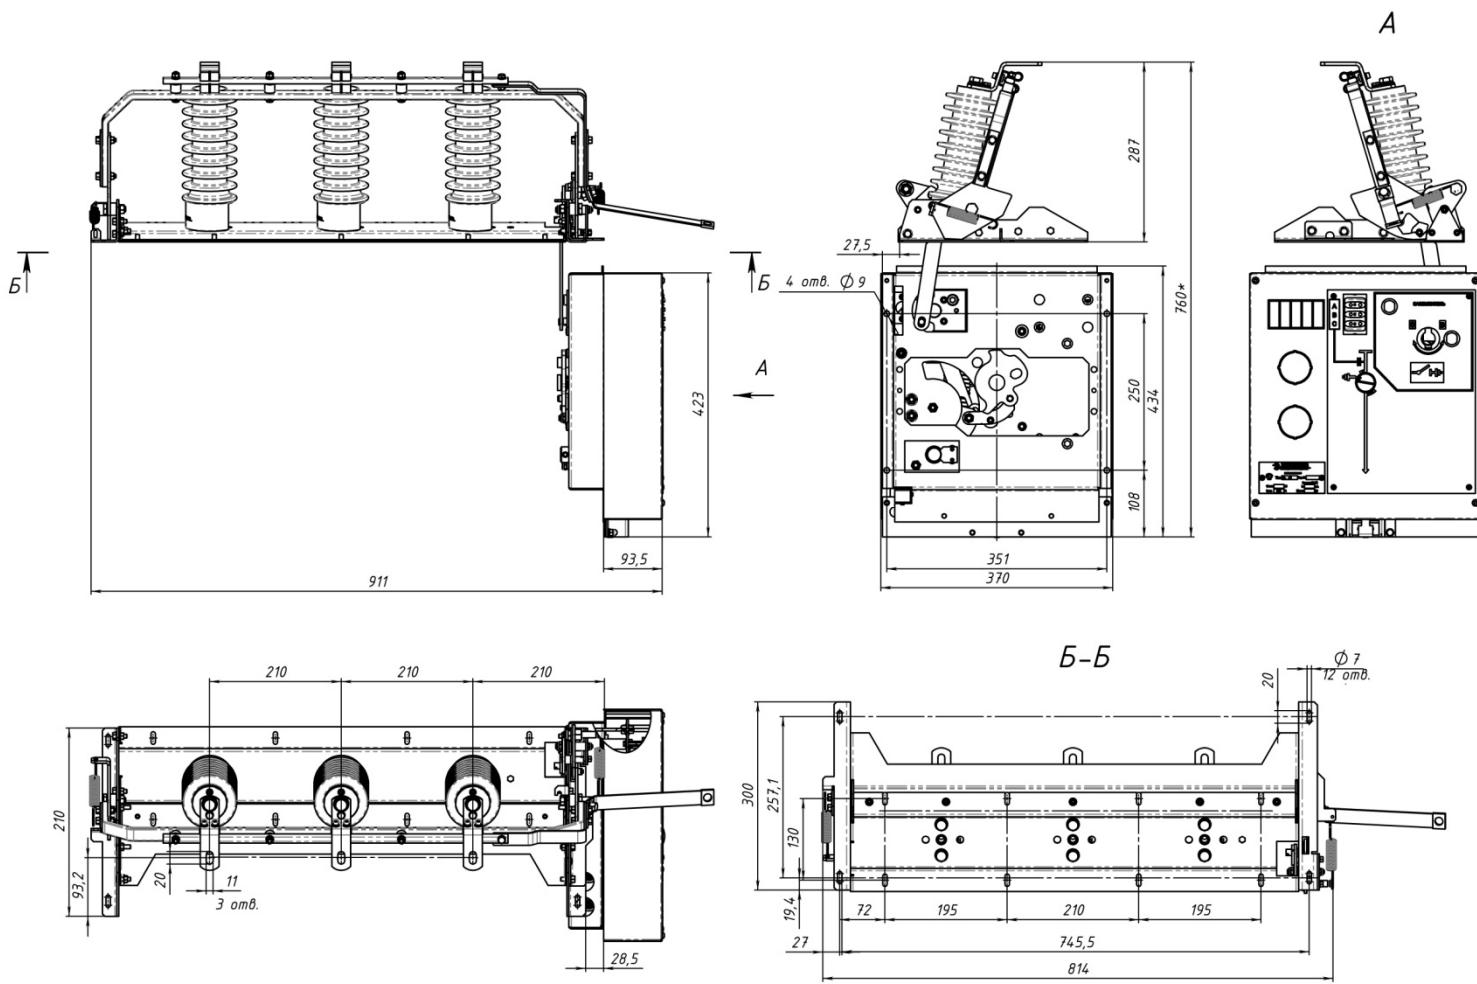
Габаритно-присоединительные размеры аппарата типов SL24-EH(C, D)
